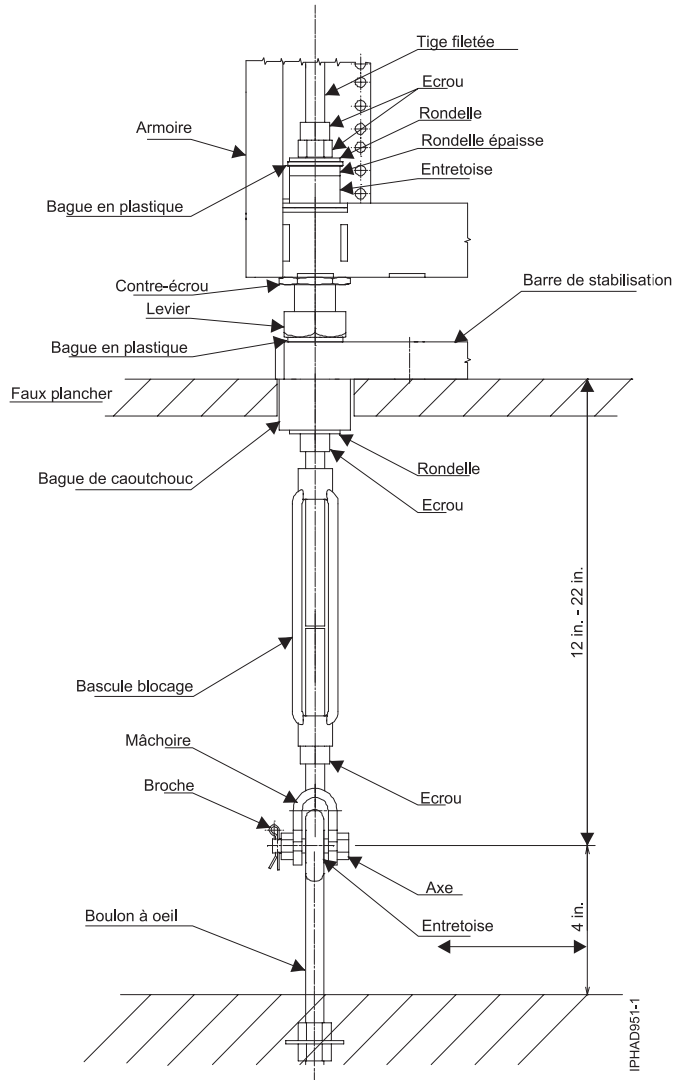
Matériel d'ancrage d'assemblage de lanterne de tendeur pour un faux plancher de 304,8 mm à 558,8 mm (44P3000)
